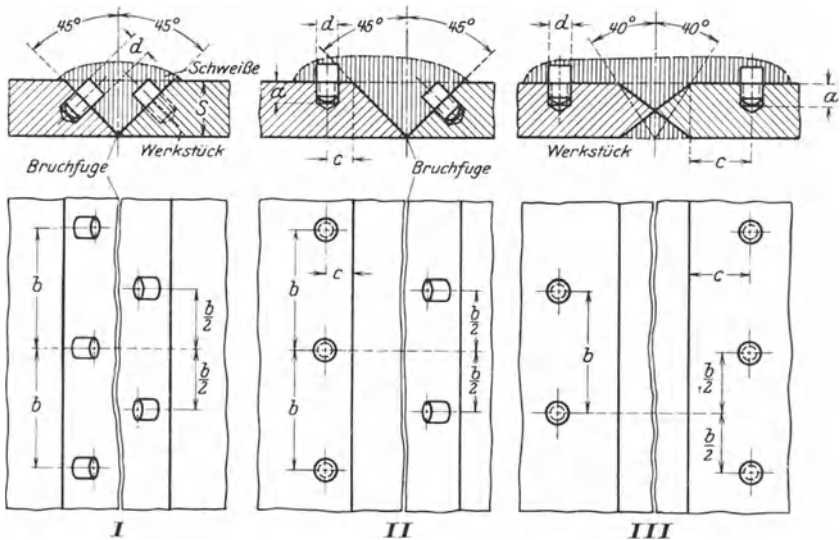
Anordnung von Stiften bei Gußeisenkaltschweißungen.
